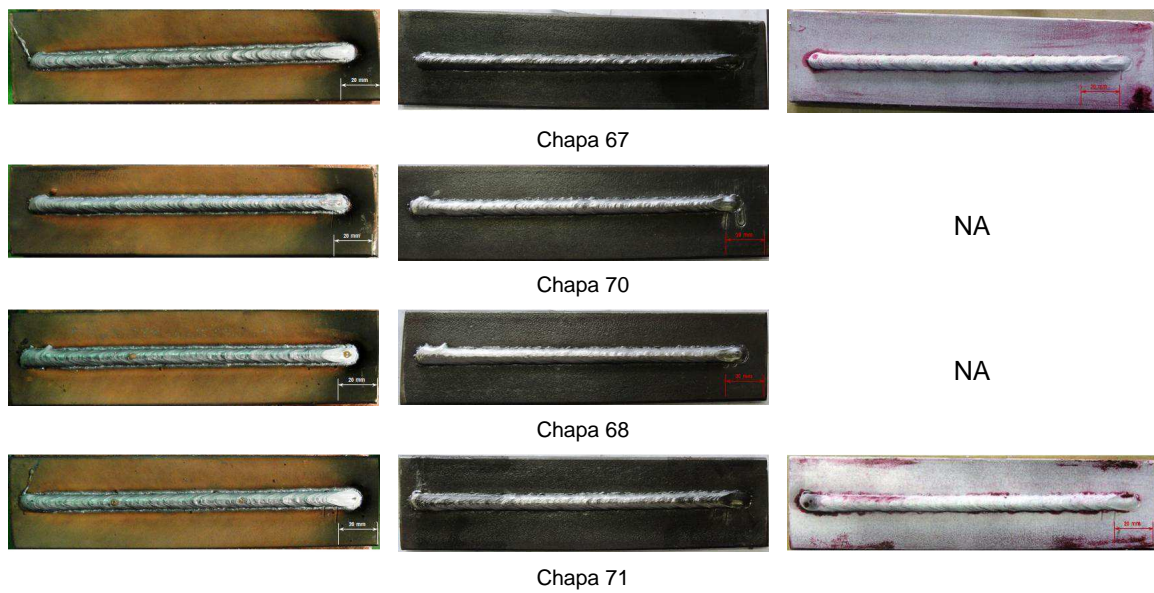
Chapas 67, 70, 68 e 71 após soldagem com Ar+8% H_2 , após preparação para ensaio visual e após ensaio por líquido penetrante.
